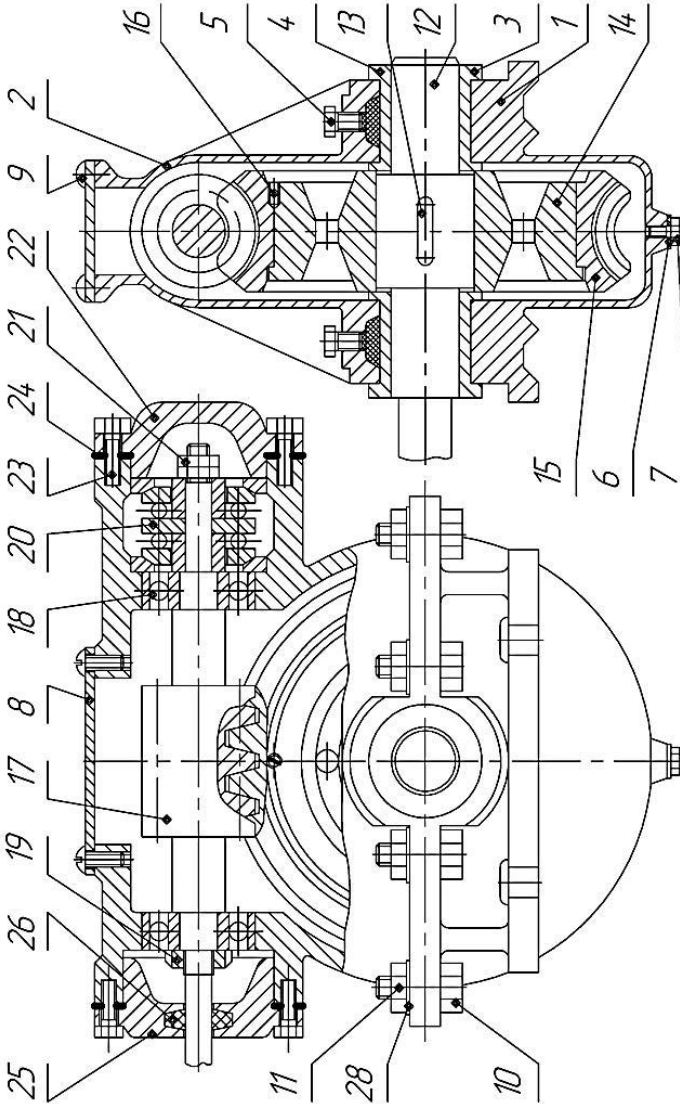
Складальне креслення черв'ячного редуктора Р05.000 СБ
